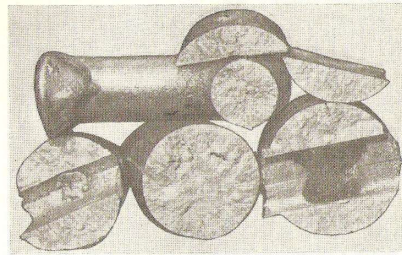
Разрез формы отливки из ферросилида с верхней литниковой системой.
